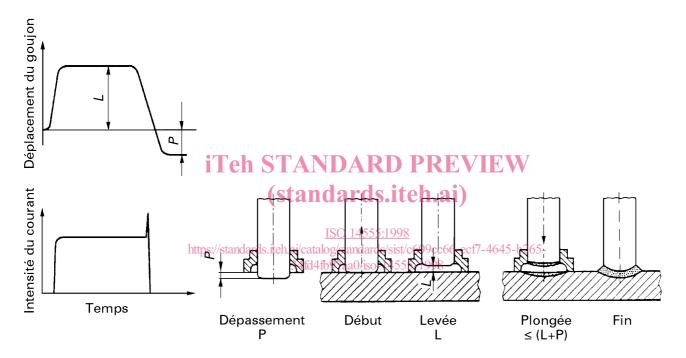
Mouvement du goujon en soudage à l'arc par fusion et forgeage
